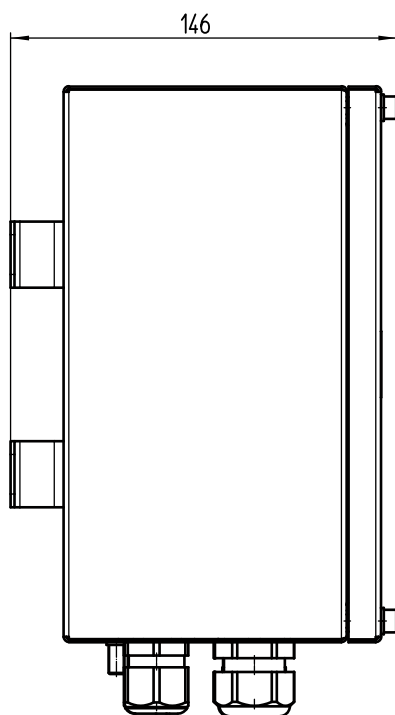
Plan de perçage du boîtier de raccordement pour VISIC100SF (toutes les cotes sont en mm)
